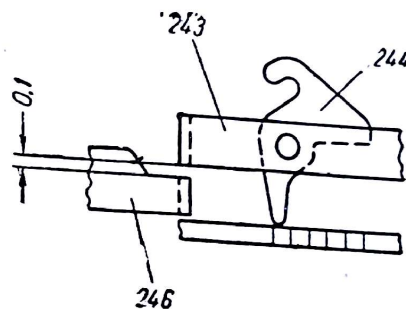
Регулировка шагового рычага 243 относительно движка 246
